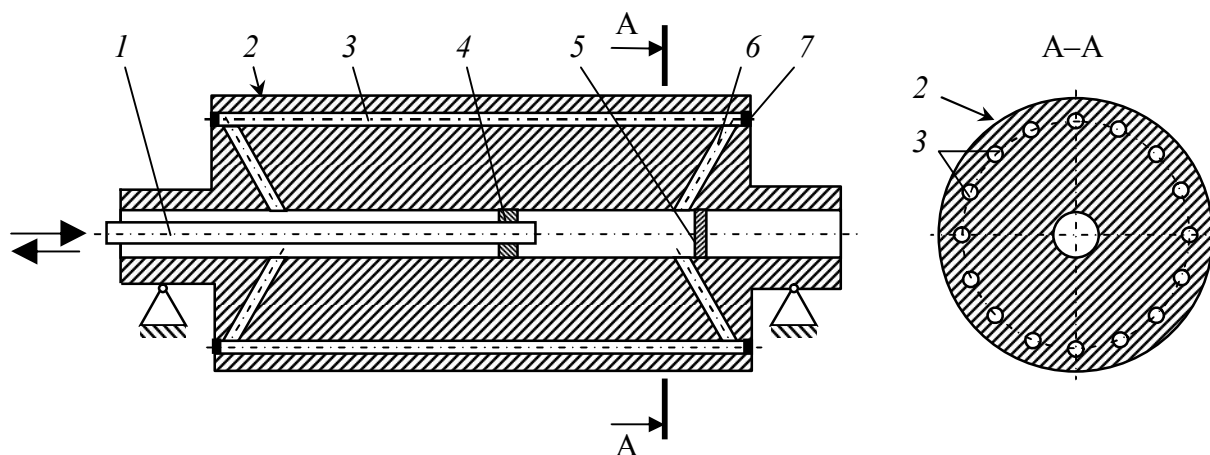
Схема валка з периферійними каналами: 1 – труба для подачі теплоносія; 2 – робоча поверхня бочки валка; 3 – периферійний канал; 4 – поршень; 5 – заглушка; 6 – похилий канал; 7 – пробка периферійного каналу
